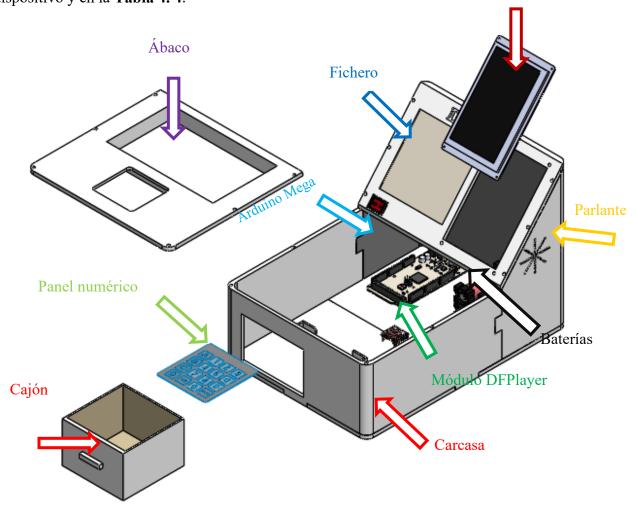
5 Vista isométrica explosionada del dispositivo alternativa 2
